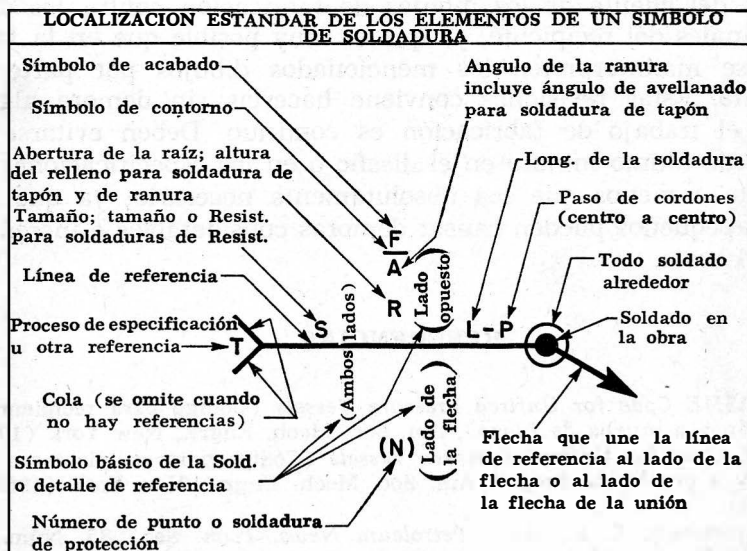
Símbolos de soldadura estándar. (Redibujados con permiso de *Welding Handbook*, American Welding Society)
